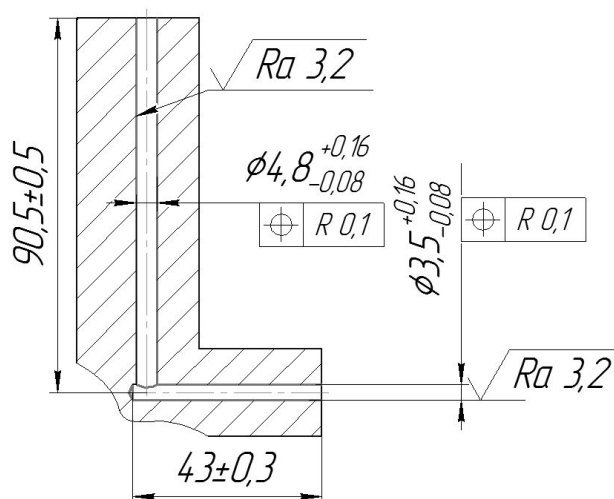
Эскиз обрабатываемых поверхностей детали «Корпус Форсунки»
